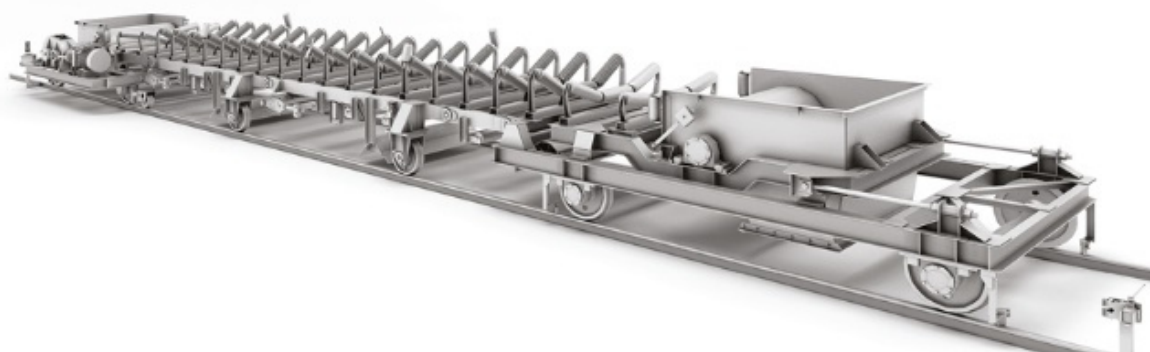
Конвейер ленточный катучий реверсивный
